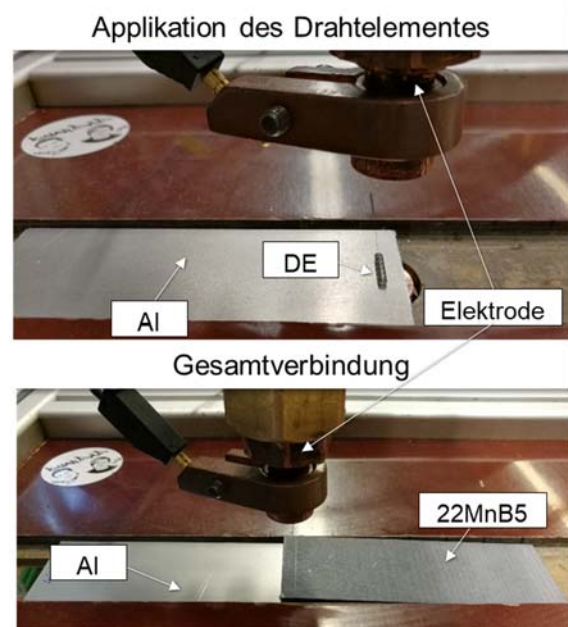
Schweißanlage (a) und Versuchsaufbau (b)
